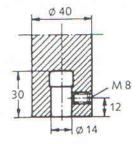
Werkzeugaufnahme JOSSI-Stempelnorm W14
